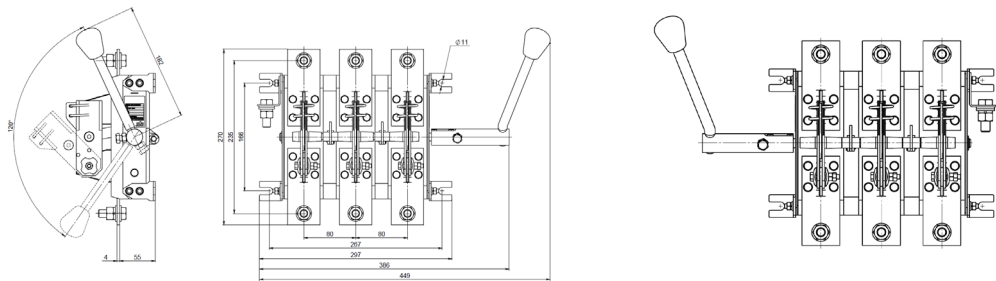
Разъединитель РЕ19-39-31160-630А-ИП УХЛЗ с рычагом для пополюсного оперирования штангой
